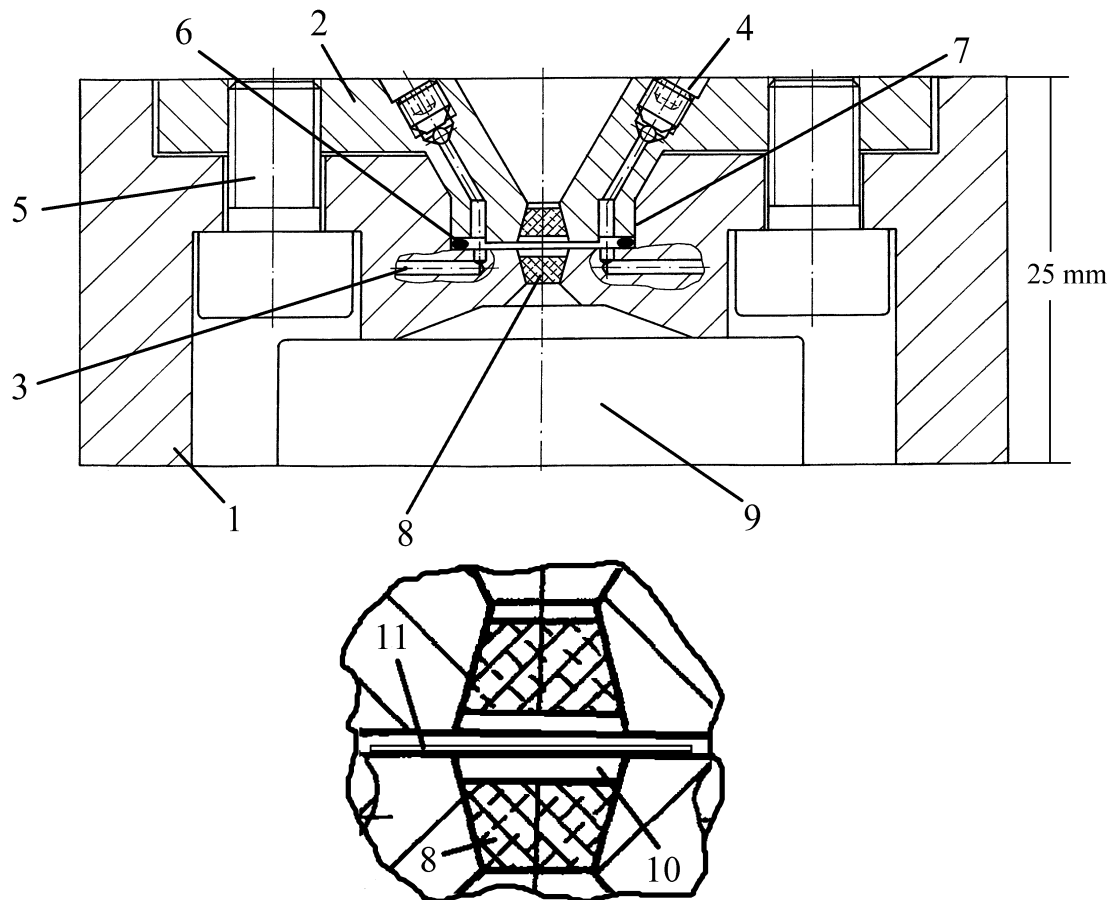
Schnitt durch die HPDS-3000-Hochdruckzelle. Oben: Vollschnitt der gesamten Zelle, unten: Detailausschnitt. (1) Unterteil; (2) Deckel; (3) Druckbohrungen; (4) Entlüftungskanäle; (5) Innensechskantschrauben 1#6; (6) O-Ring; (7) progressive Metallabdichtung; (8) Saphirscheiben (9) Zugangsbereich für die Objektive; (10) abgetrennter Raum; (11) transparente Abdeckung. [112, 113]
